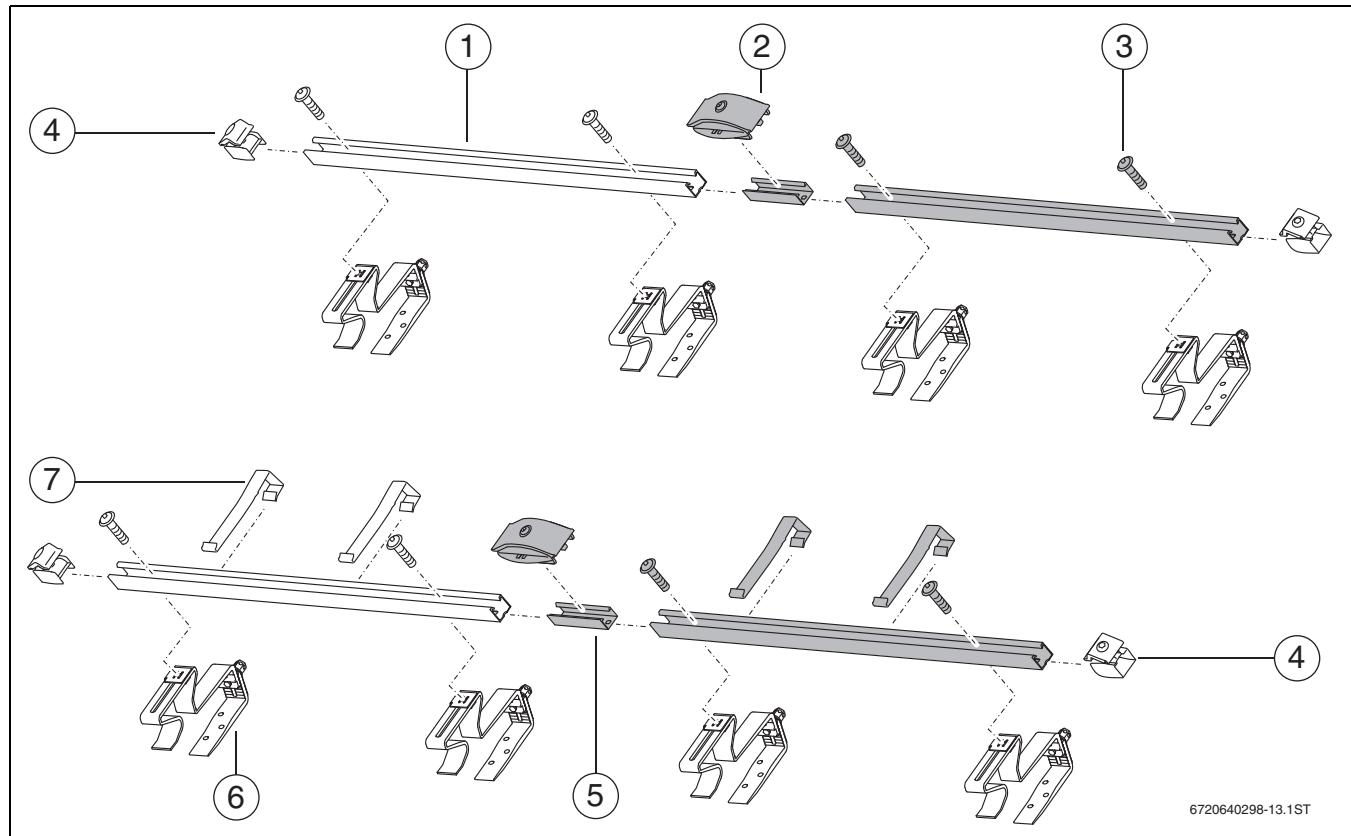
Set di fissaggio/montaggio per 2 collettori: 1 set di fissaggio/montaggio di base, 1 set di fissaggio/montaggio di ampliamento (grigio) e 2 set di fissaggio/montaggio per tegole
